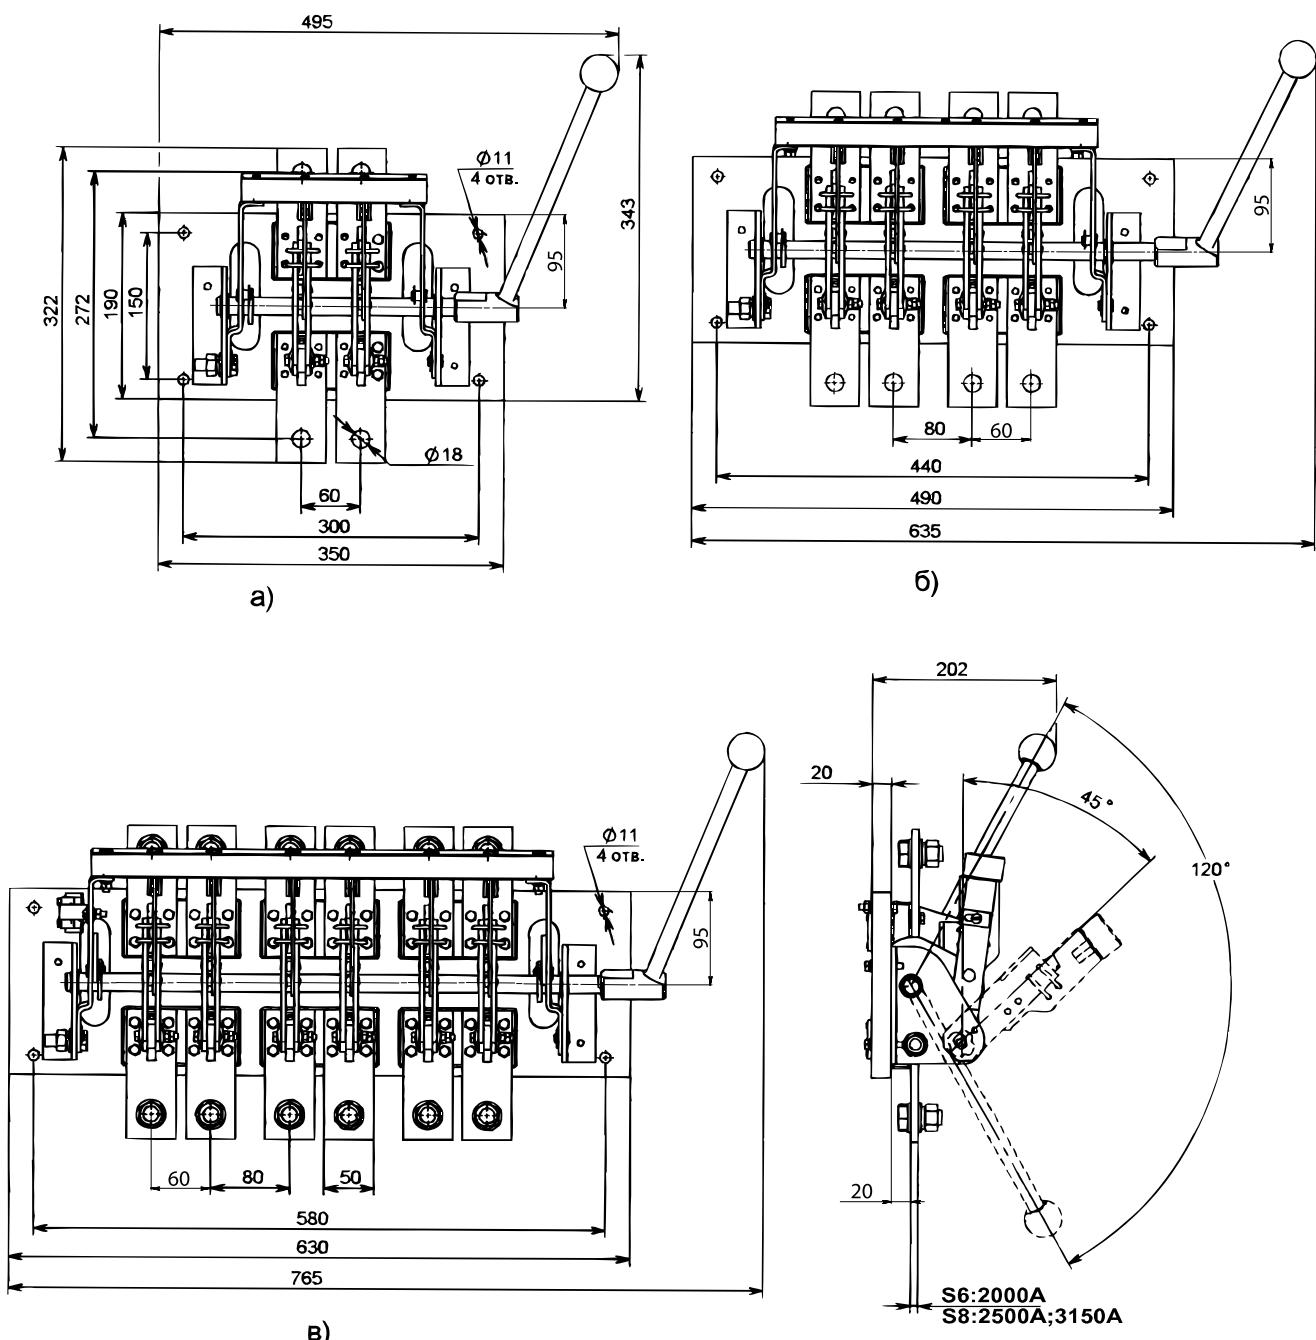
Разъединитель РЕ19 с боковой рукояткой
